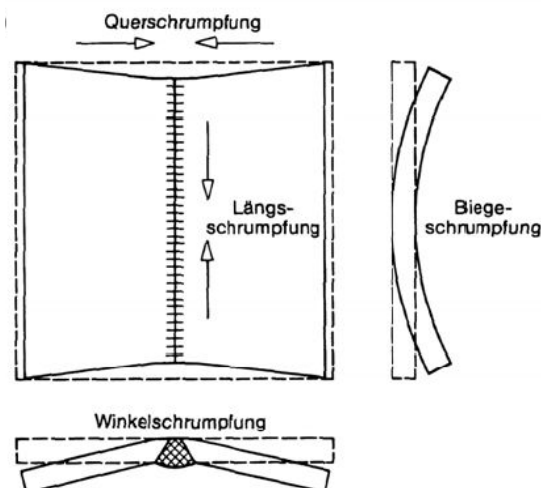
Schrumpfformen beim Schweißen [37]
